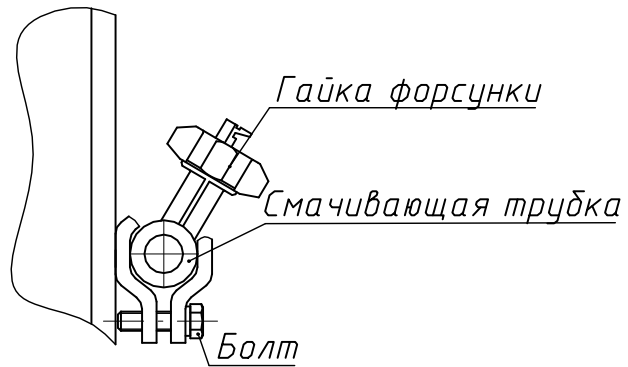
Регулировка направления потока смачивающей жидкости.
